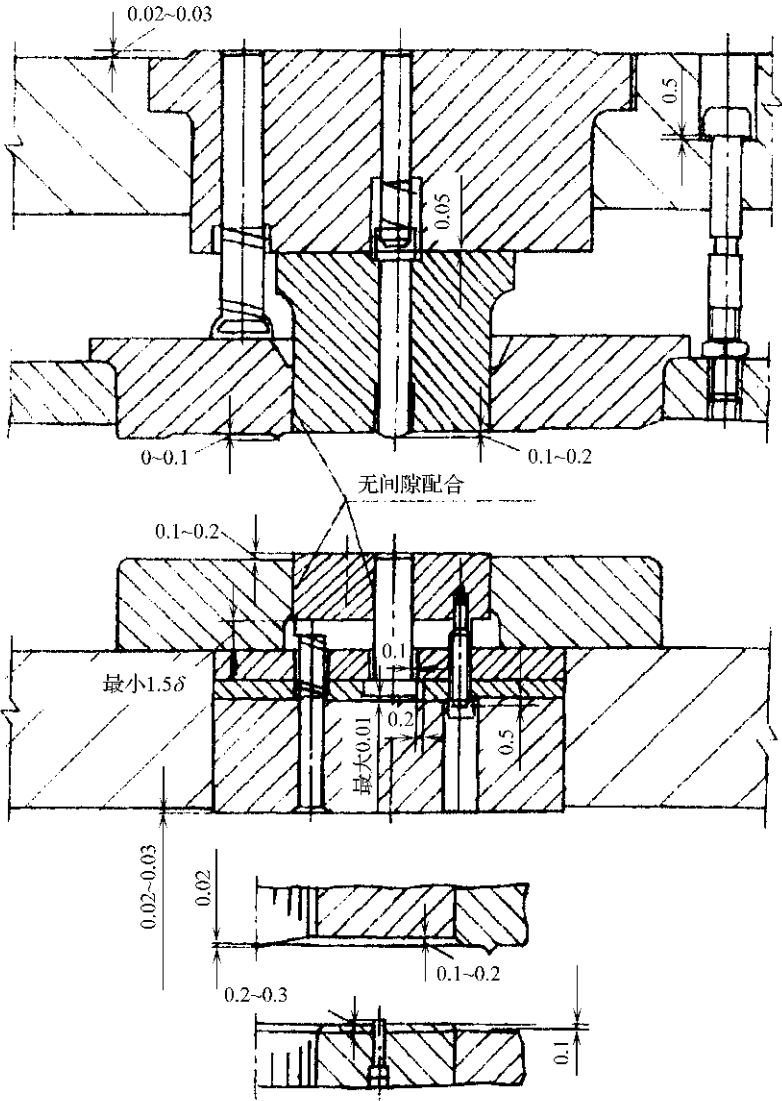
11 固定凸模式模具零件间的配合和尺寸要求
